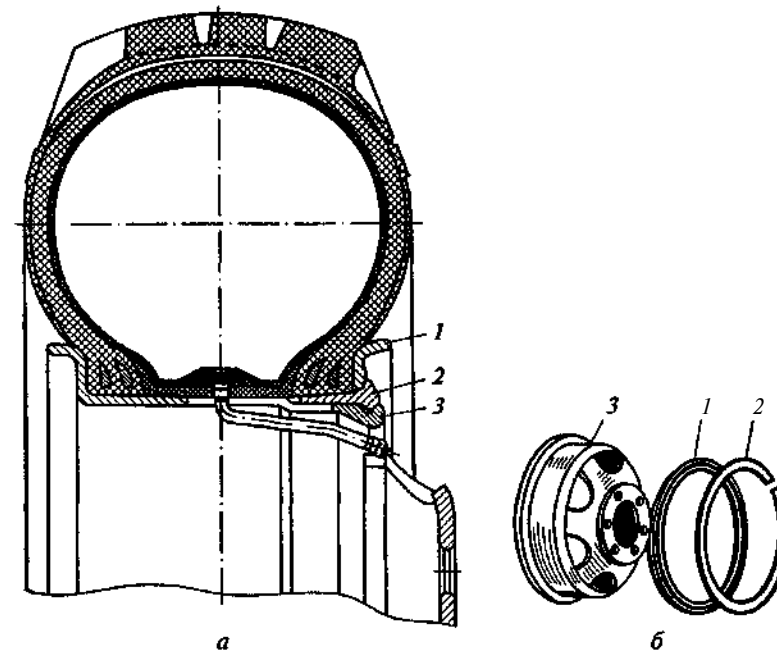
Дисковое колесо грузового автомобиля: 1 — бортовое кольцо; 2 — разрезное кольцо; 3 — обод
